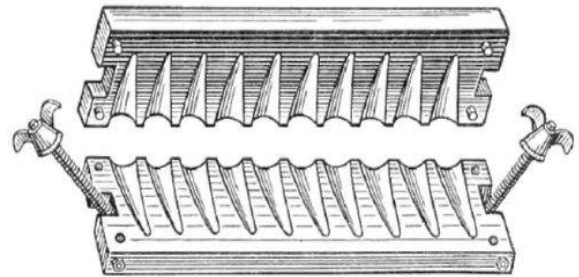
Фрезерована форма для виливки супозиторіїв
